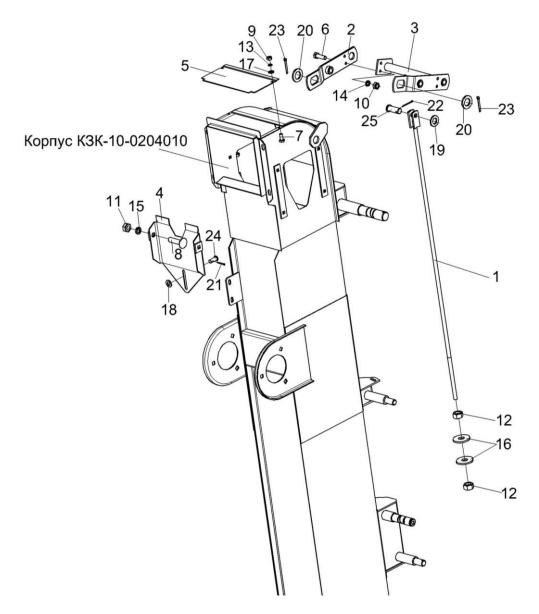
Элеватор зерновой КЗК-10-0214000 (лист 3)
